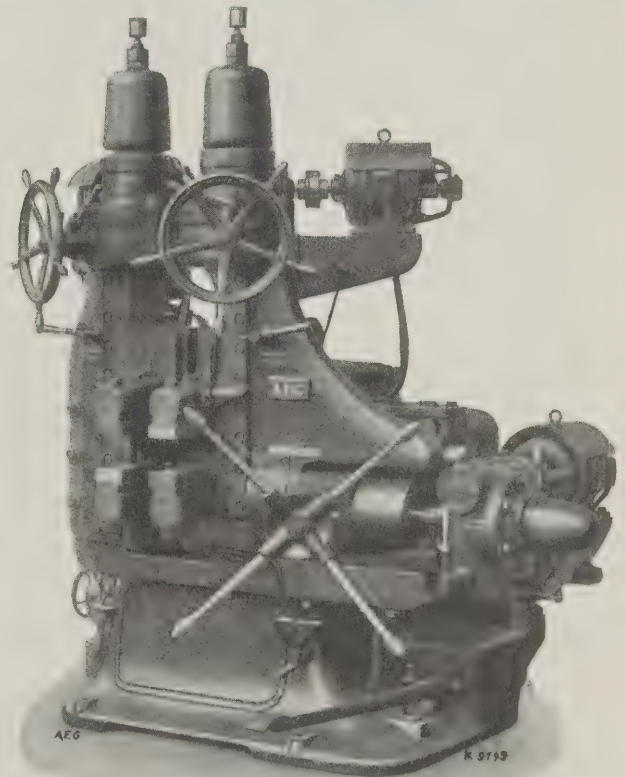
Stumpfschweißmaschine SRWM 80/140 mit motorischer Einspann- und Stauchvorrichtung.
